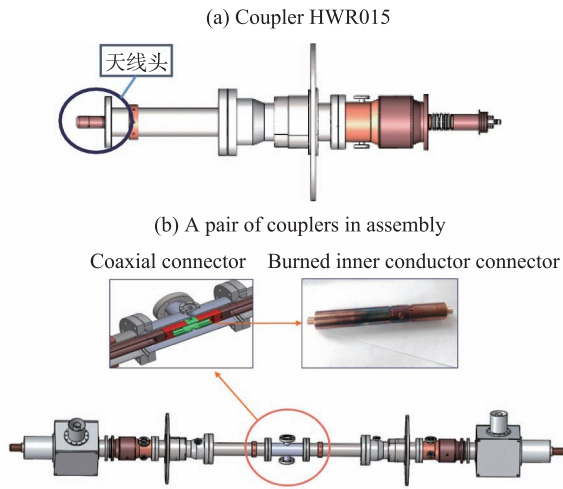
(在线彩图) HWR015 耦合器 (a) 及其测试平台装配图 (b)
